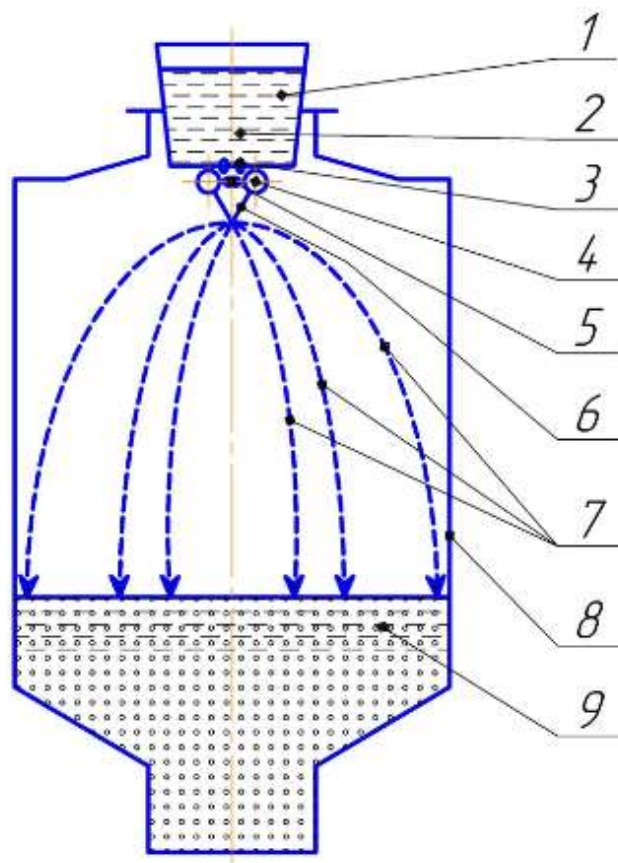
Схема отримання дробу за допомогою енергоносіїв (газу): 1 – проміжний ківш; 2 – рідкий метал; 3 – розливальний стакан; 4 – колектор; 5 - струмінь розплавлення; 6 – потоки енергоносія; 7 – траєкторія падіння гранул; 8 – розпилювальна камера; 9 – охолоджувальна вода
